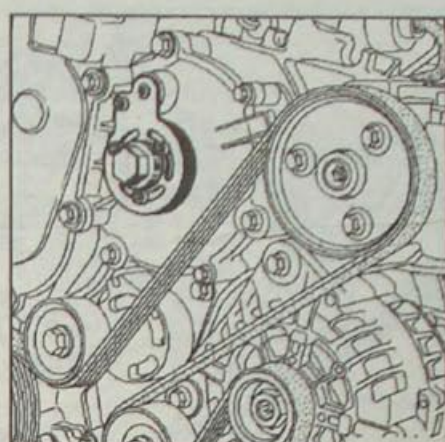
Установка на двигатель приспособления Mot. 1548 с центрирующей втулкой
